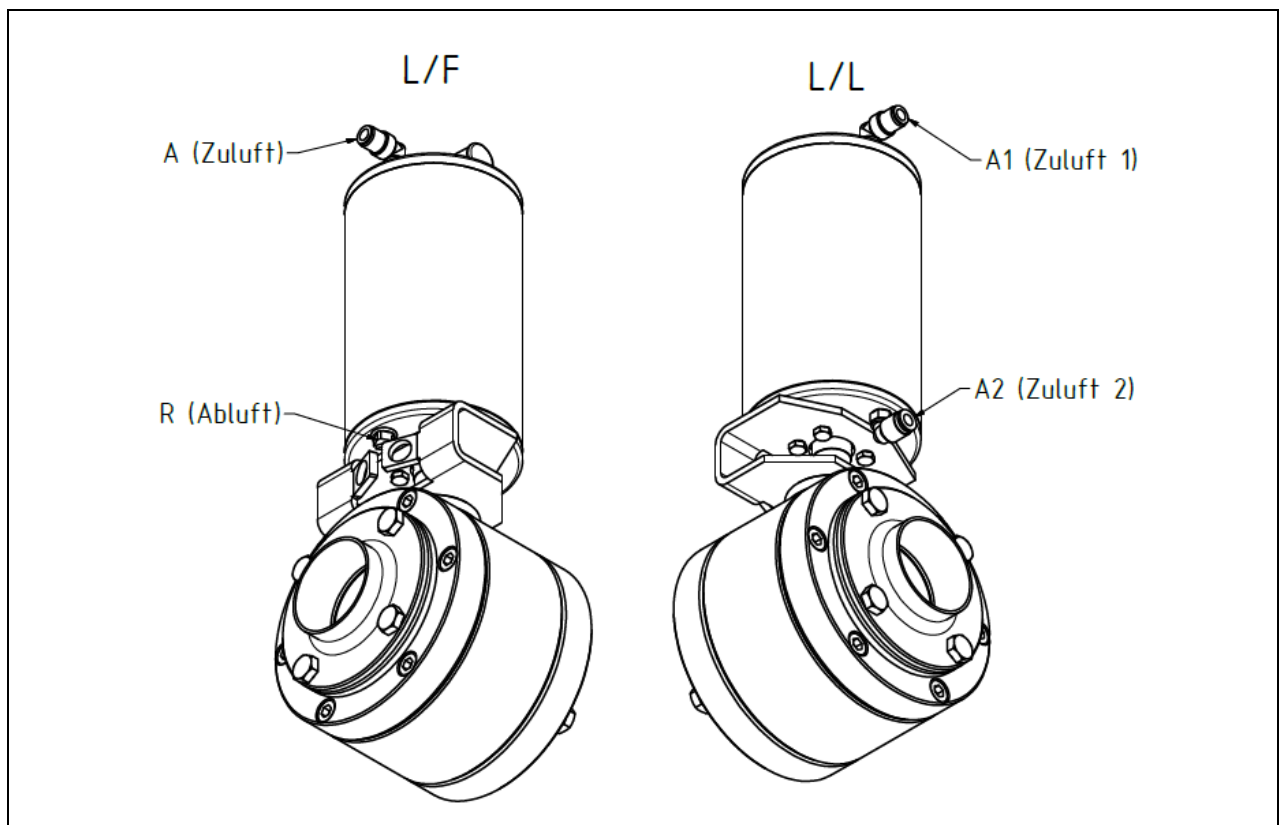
Kugelventil mit pneum. Antrieb: Steuerluftanschlüsse
